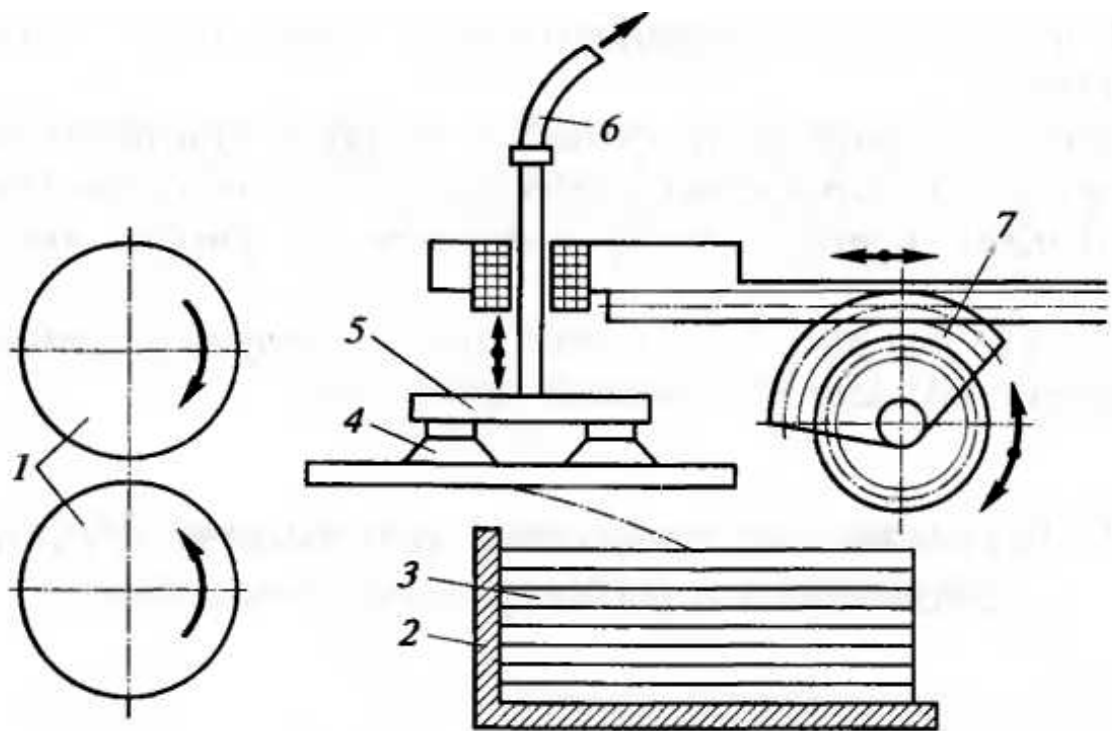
Вакуумний пристрій для відокремлення деталей з пачки:
